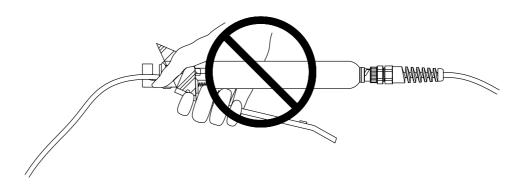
Technique incorrecte de maintien de la tête de soudure
